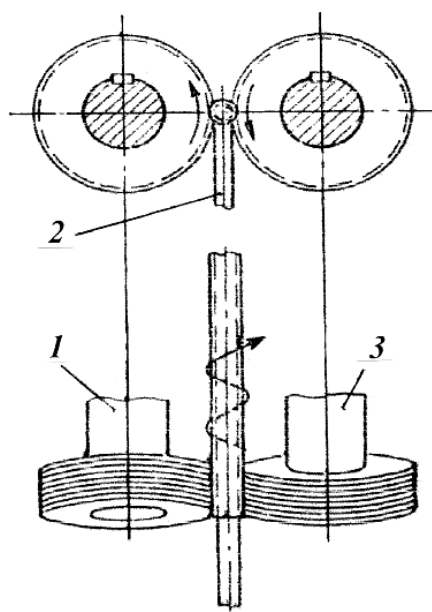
Схема накатывания резьбы с осевой подачей: 1,3 - резьбонакатные ролики, 2- опора.
